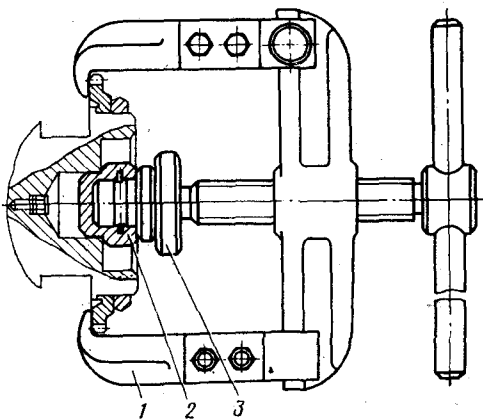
Снятие ведущей шестерни привода масляного насоса и переднего противовеса с коленчатого вала:
